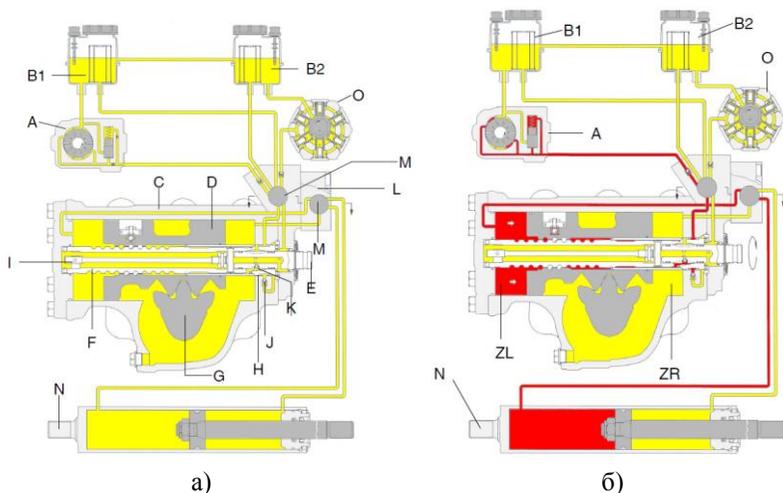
Двухконтурный гидравлический усилитель руля с двумя насосами и однопоршнемвым вспомогательным цилиндром:
